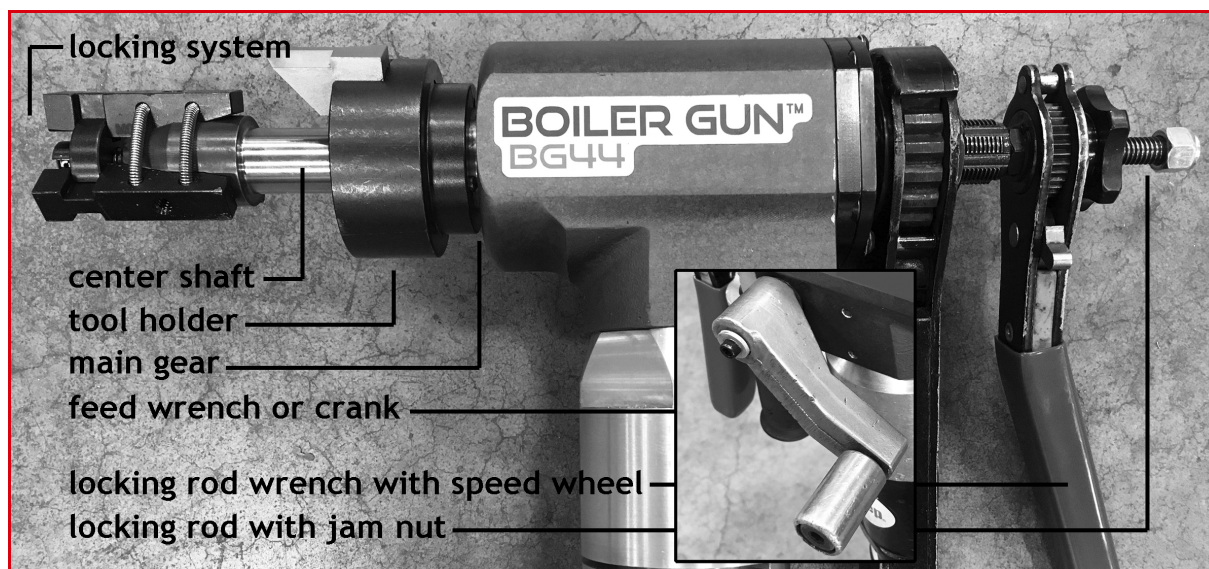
PRINCIPAUX COMPOSANTS DE LA BG44 BOILER GUN
